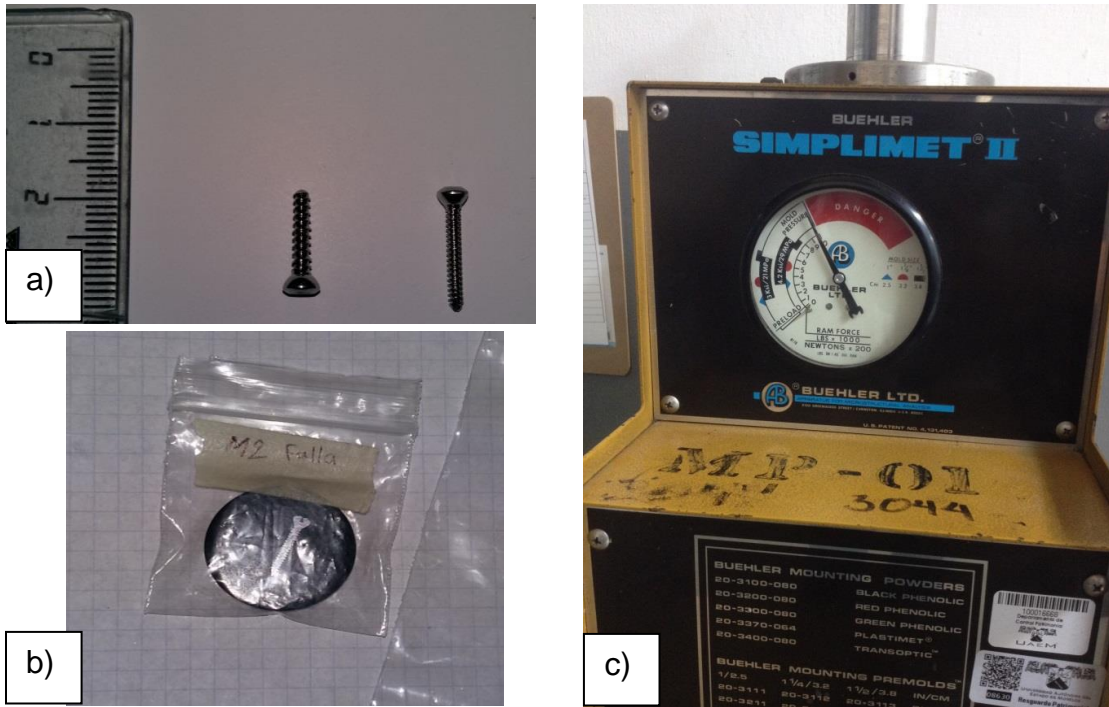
a) Tornillos de implante con cota b) Muestra montada y pulida c) Montadora de muestras.
